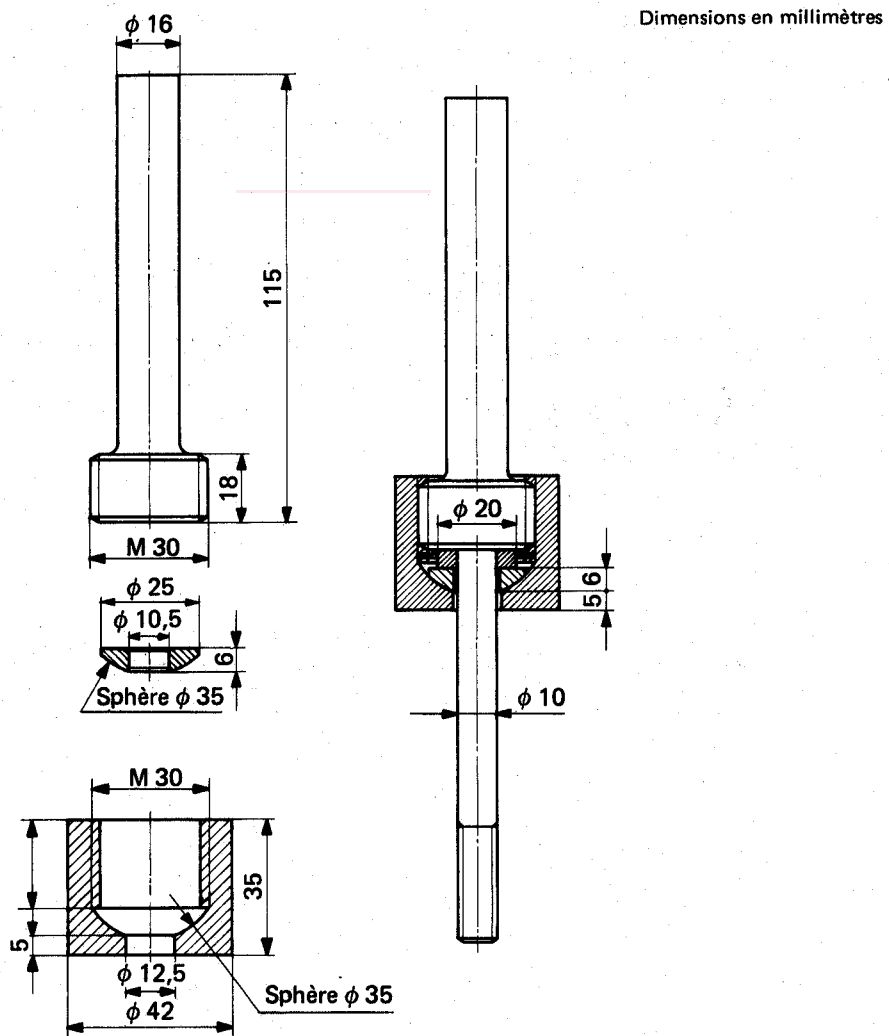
Montage pour la mise en charge par traction des éprouvettes type I
